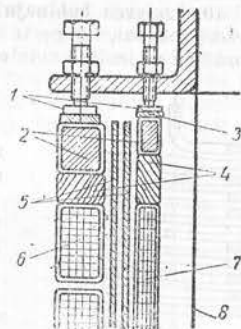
Izolarea și consolidarea față de jug: 1 — placă de fier; 2 — inel din fier izolat; 3 — pertinax; 4 — lemn; 5 — cilindru din preșpan; 6 — bobinaj de înaltă tensiune; 7 — bobinaj de joasă tensiune; 8 — miezul magnetic.
